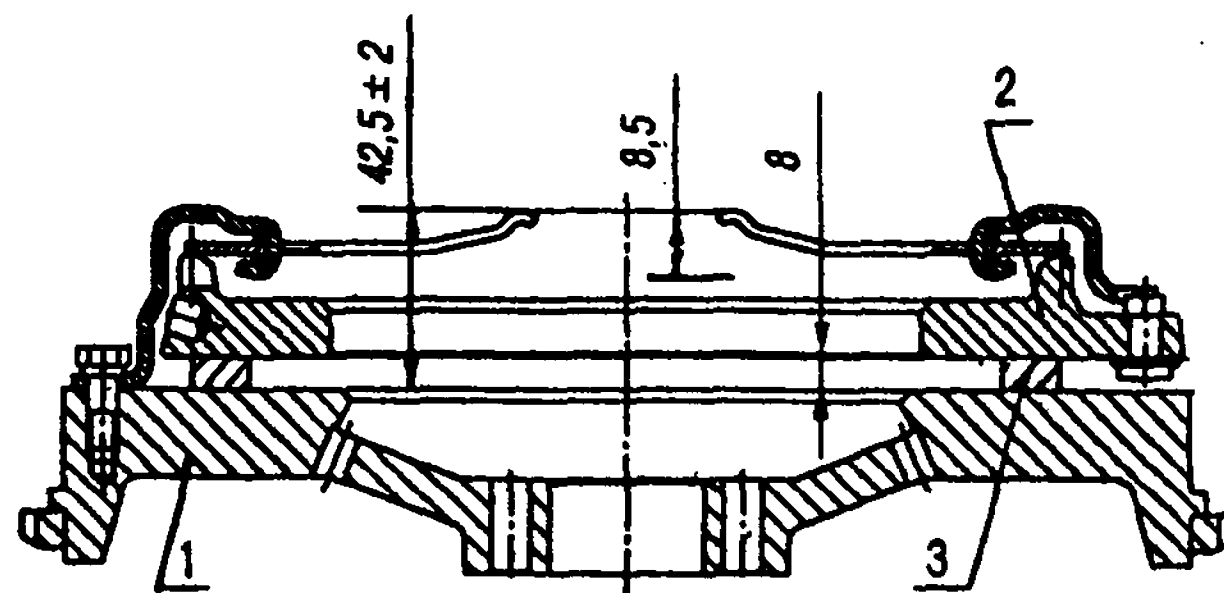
Регулировка концов лепестков и проверка нажимного усилия: 1 - маховик; 2 - нажимной диск; 3 - шайба
